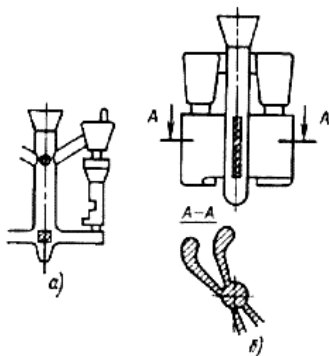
Литниково-питающая система типа VII (местная прибыль над каждой отливкой и коллектор): *a* – четырехместная при центральном расположении стояка; *б* – заливка лопаток через вертикальный щелевой питатель
